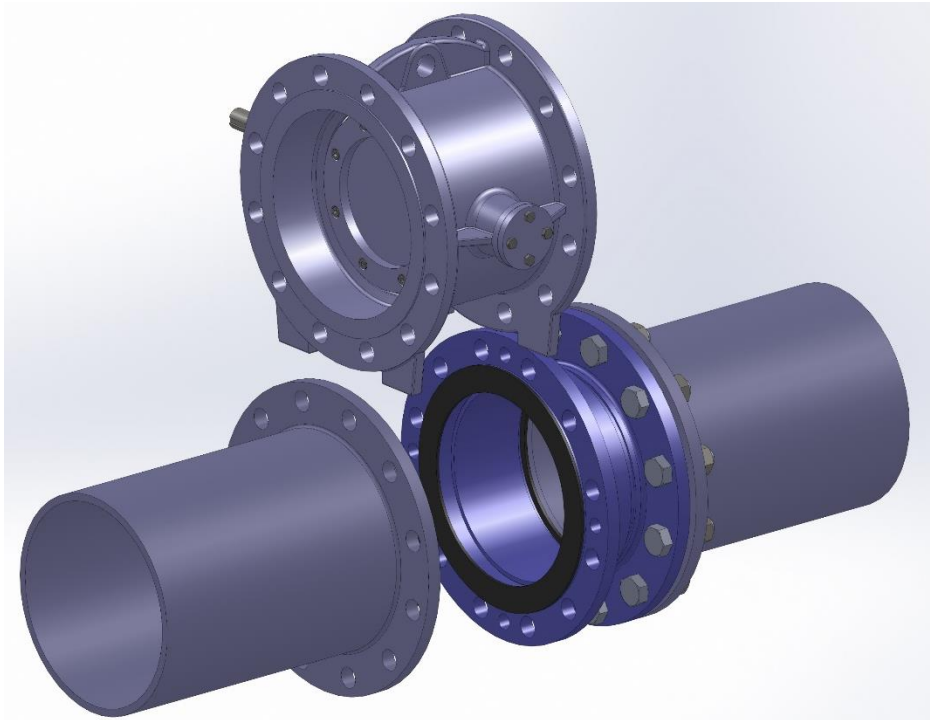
Geleneksel Demontaj Sistemi (Traditional Disassembly Process)
